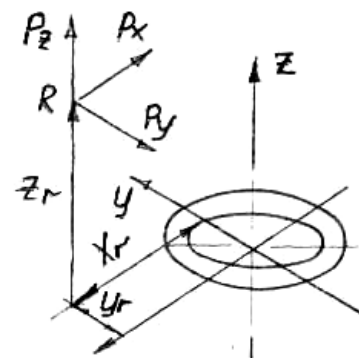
Розрахункова схема зубчастого фіксаторного пристрою
